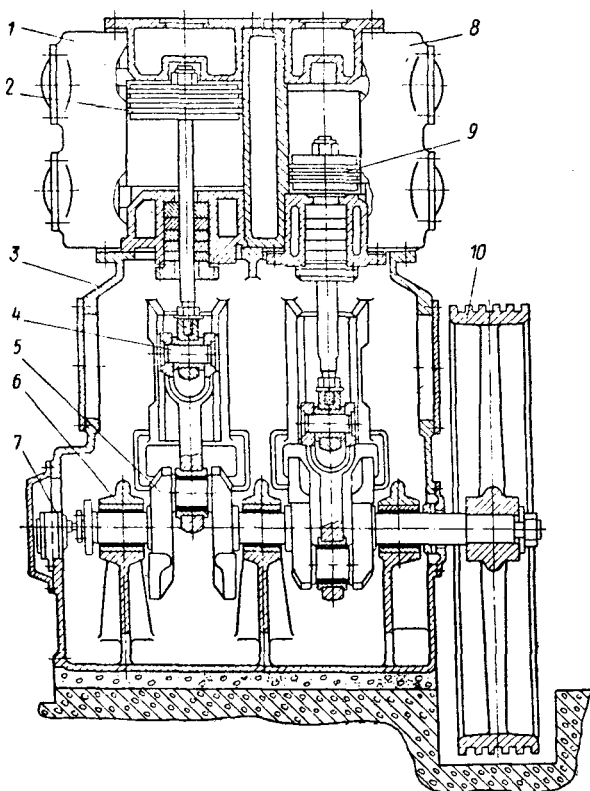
Вертикальный двухрядный двухступенчатый компрессор:
